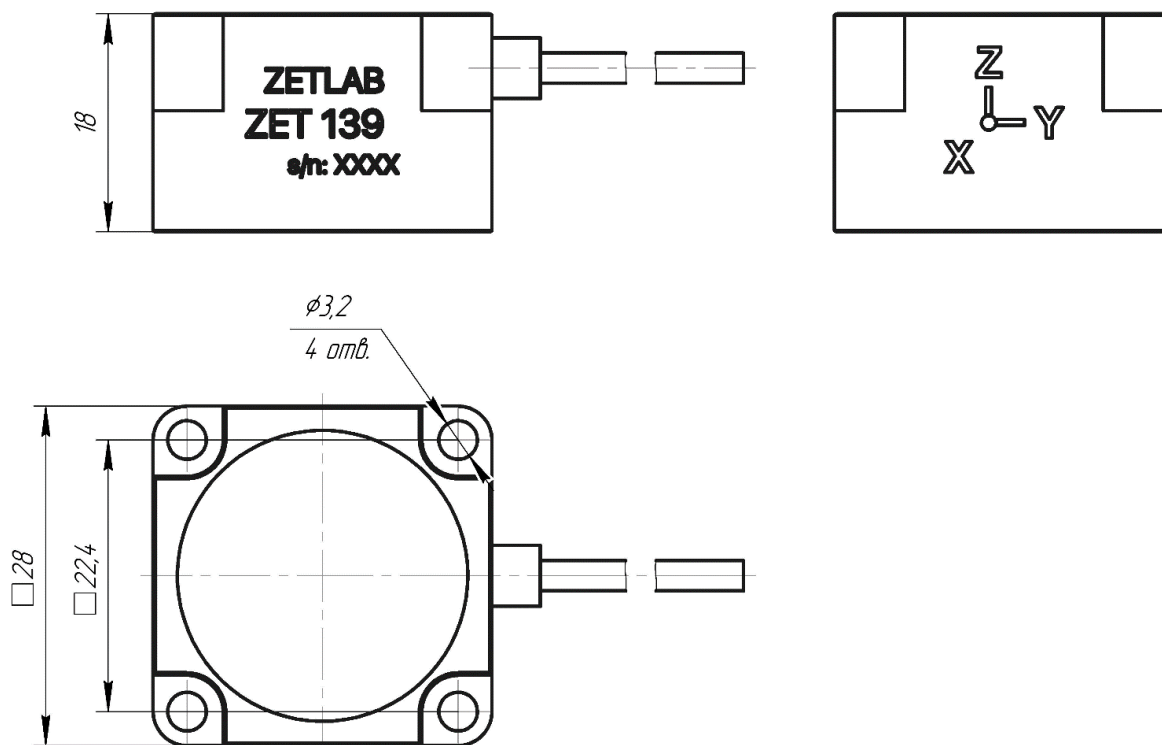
Габаритный чертеж вибропреобразователя ZET 139
